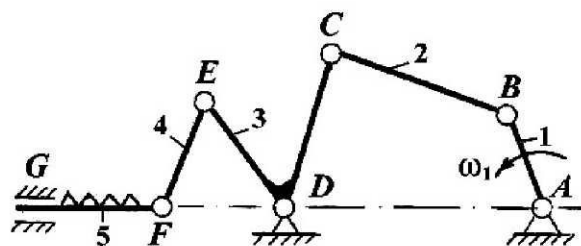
Механизм привода режущего аппарата зерноуборочного комбайна
